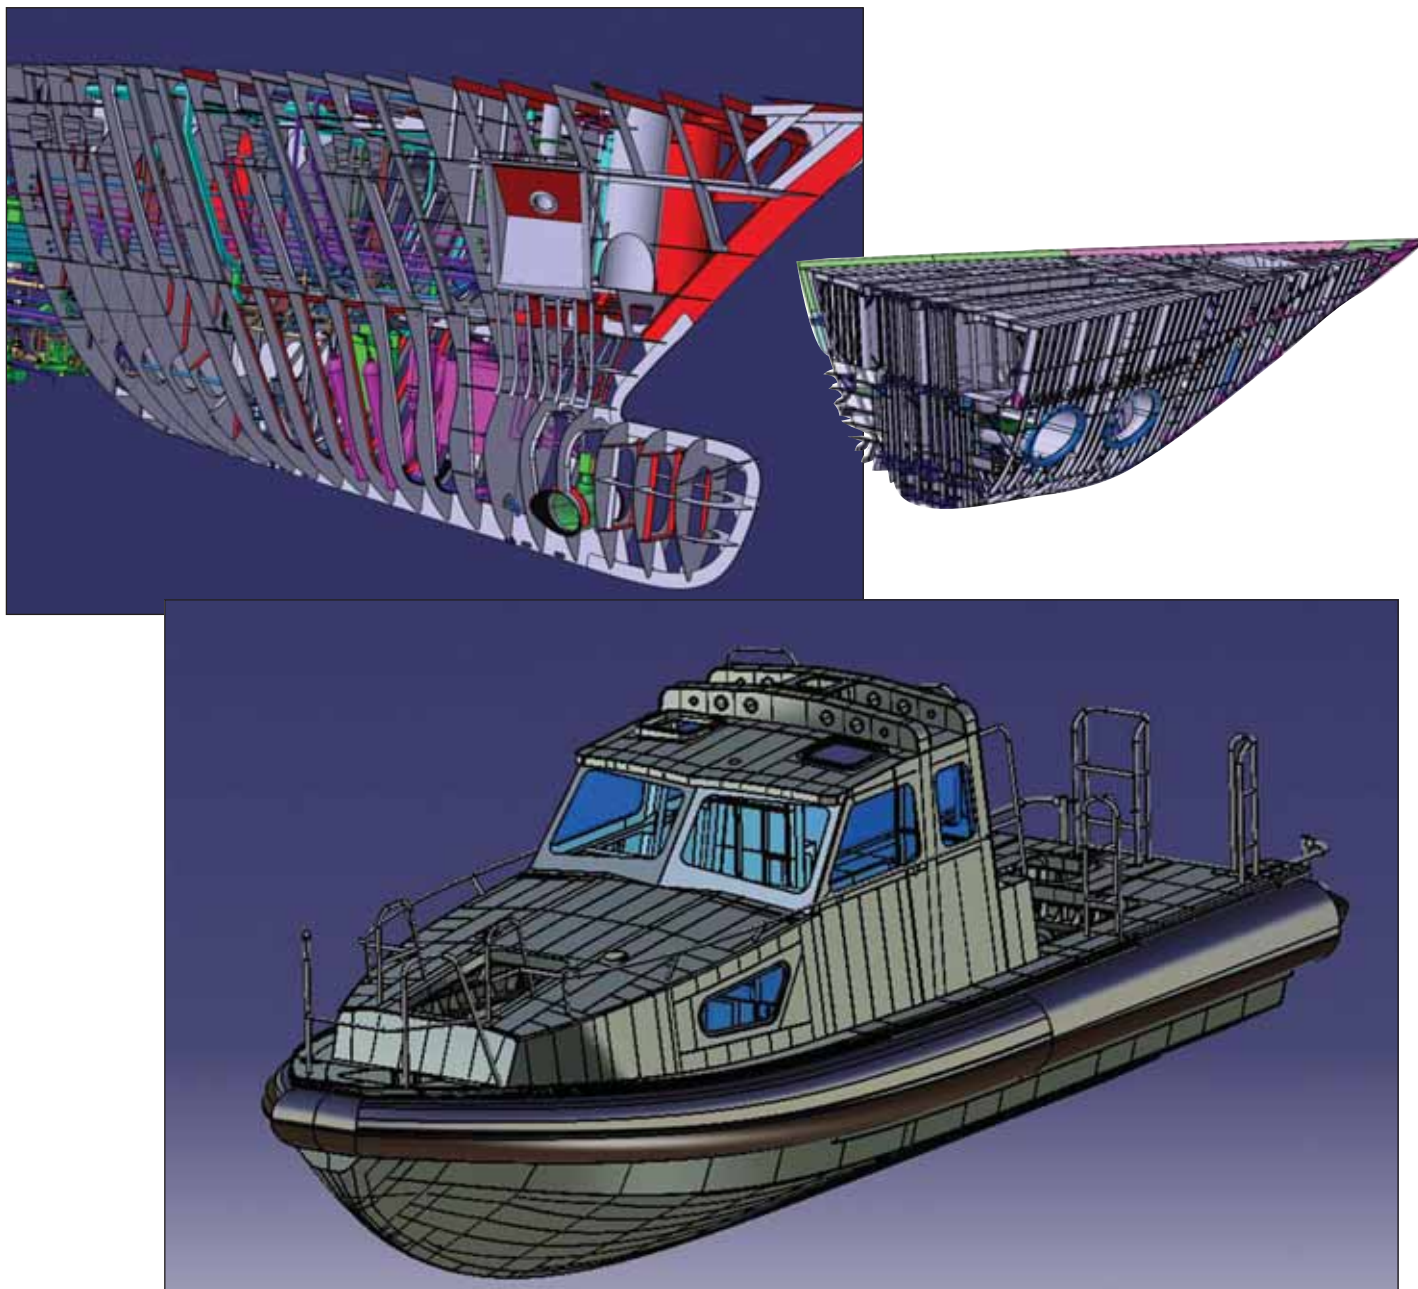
Примеры корпусных конструкций и изделий «МП "Звездочка"»
